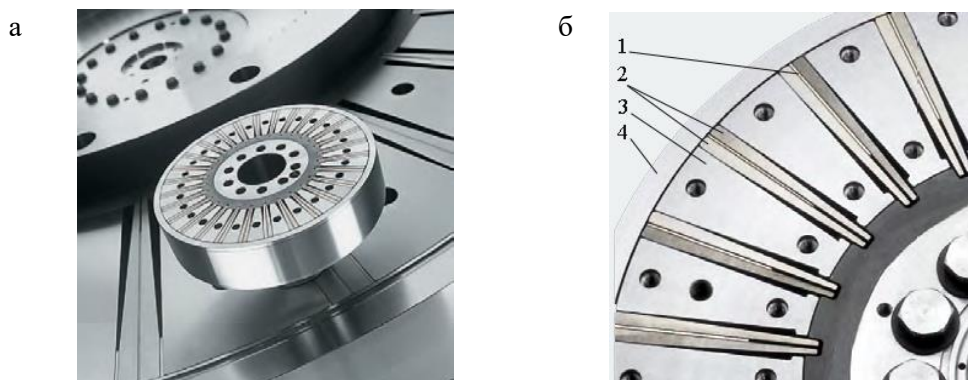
Пружинный демпфер крутильных колебаний «Geislinger» [9]: а – общий вид, б – конструкция; 1 – промежуточная вставка между рессорными пружинами, 2 – рессорные пружины, 3 – сектор маховой массы, 4 – внешний обод (корпус) демпфера
